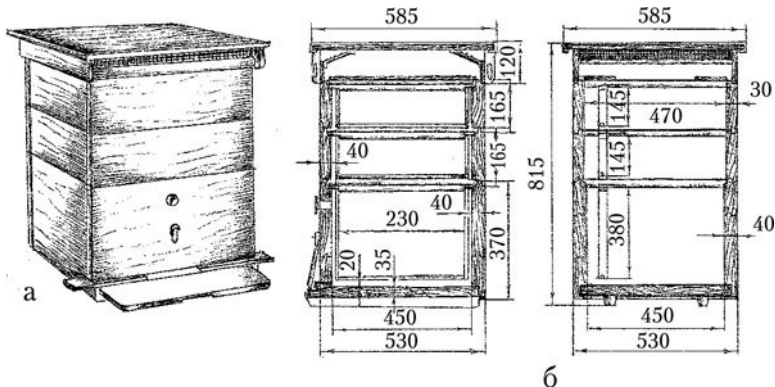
Двухкорпусный улей (размеры в мм): а – общий вид; б – устройство улья
